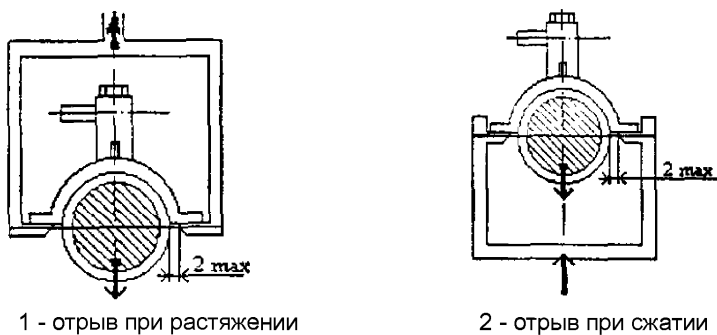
Схемы испытания седлового отвода на отрыв.
